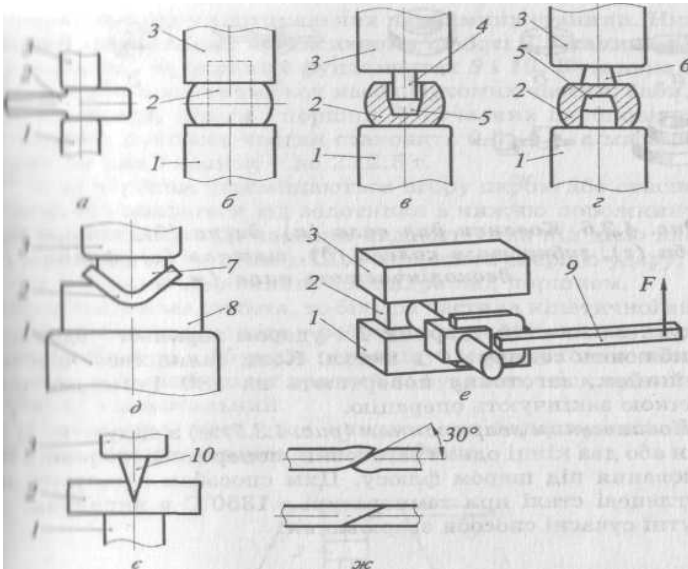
Схеми видовження (а); сплющування (б); пробивання (в,г); гнуття (д); кручення (е); рубання (є) і ковальського зварювання (ж): 1- нижній ударник; 2 — заготовка; 3 - верхній ударник; 4 - надставка; 5, 6 - прошивень; 7, 8- половини підкладного штампа; 9 - вилка; 10 - сокира; F – сила.
